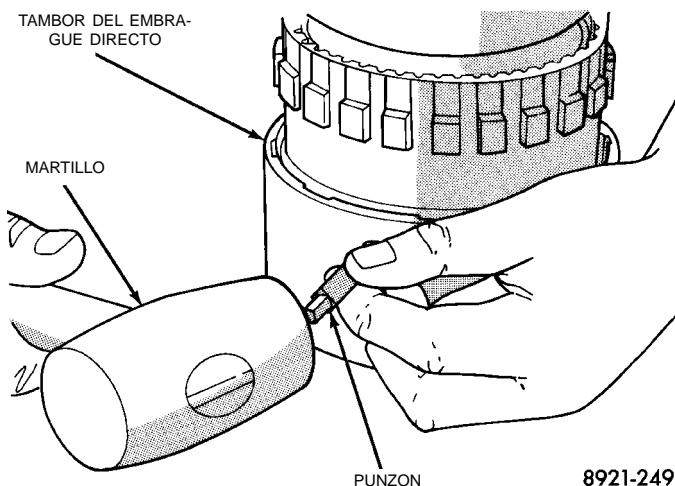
Marcas del tambor del embrague directo y el engranaje anular para su alineación durante el ensamblaje
